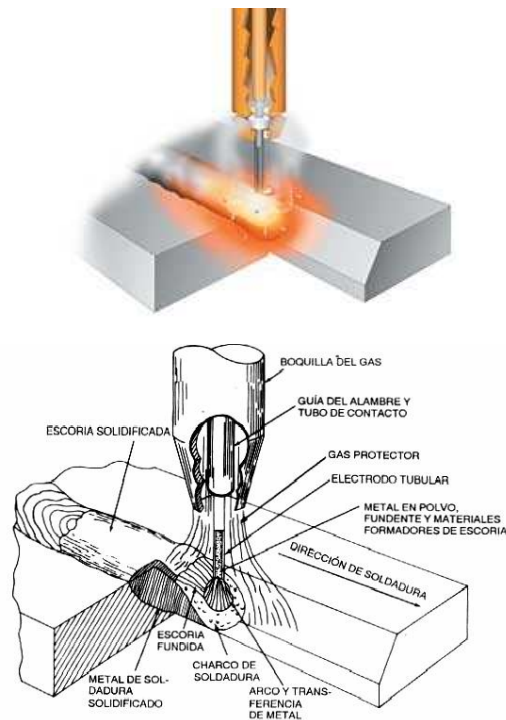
Soldadura por arco con núcleo de fundente (FCAW)
